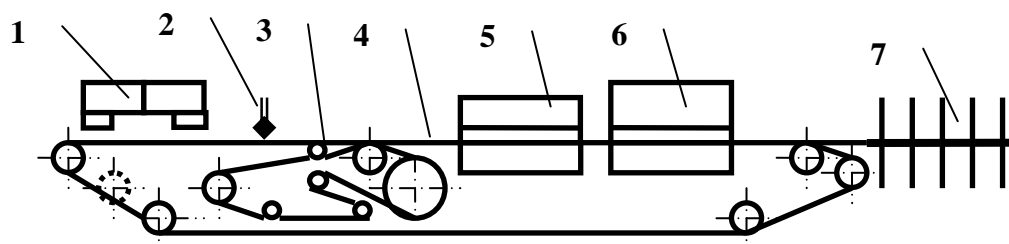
Схема главного конвейера с одноэтажной прессовой установкой (прессование с сетчатыми поддонами): 1 – формирующая станция; 2 – установка для разделения ковра; 3 – формирующий конвейер; 4 – цепной конвейер; 5 – пресс для подпрессовки пакетов; 6 – горячий пресс; 7 – веерный охладитель
